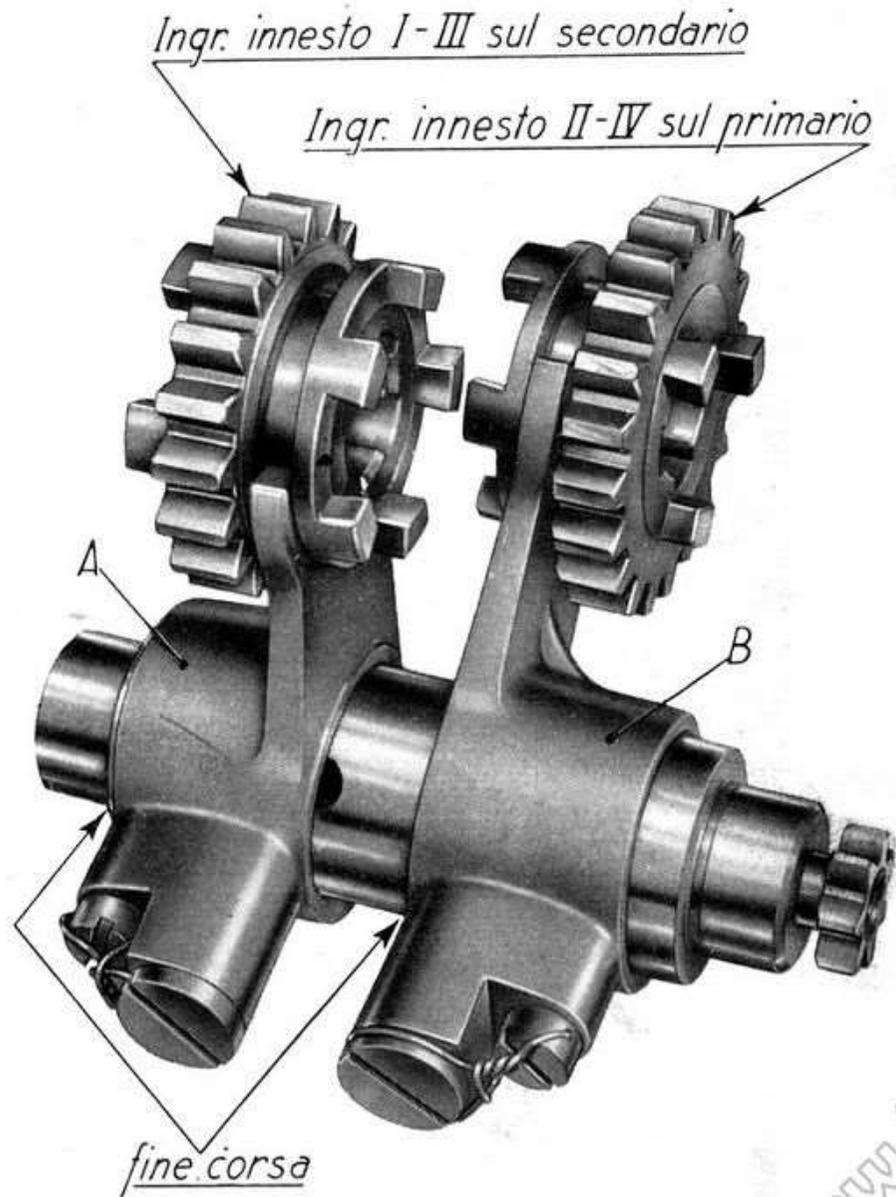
Come viene montato il gruppo tamburo-forcellini.
